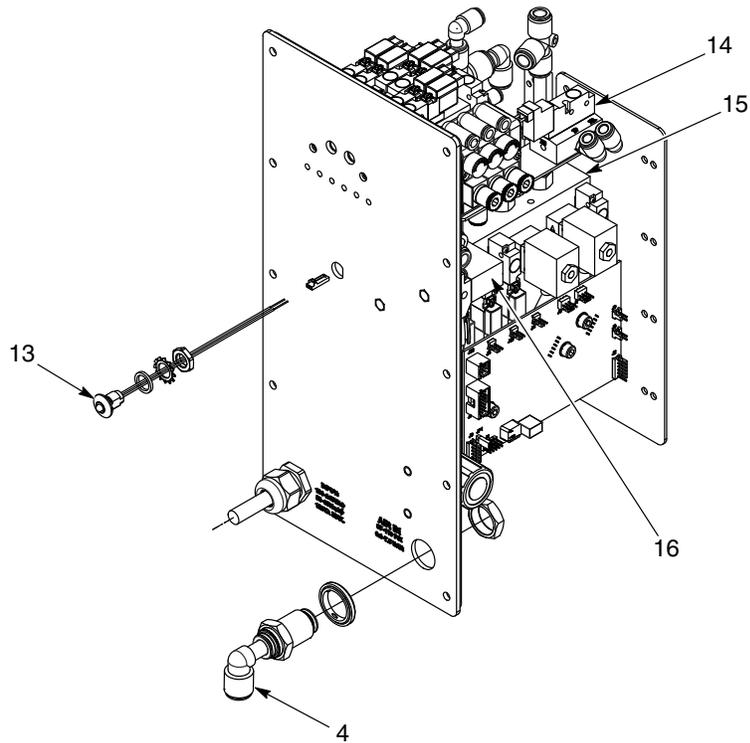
Pièces de l'ensemble panneau (1 sur 3)
